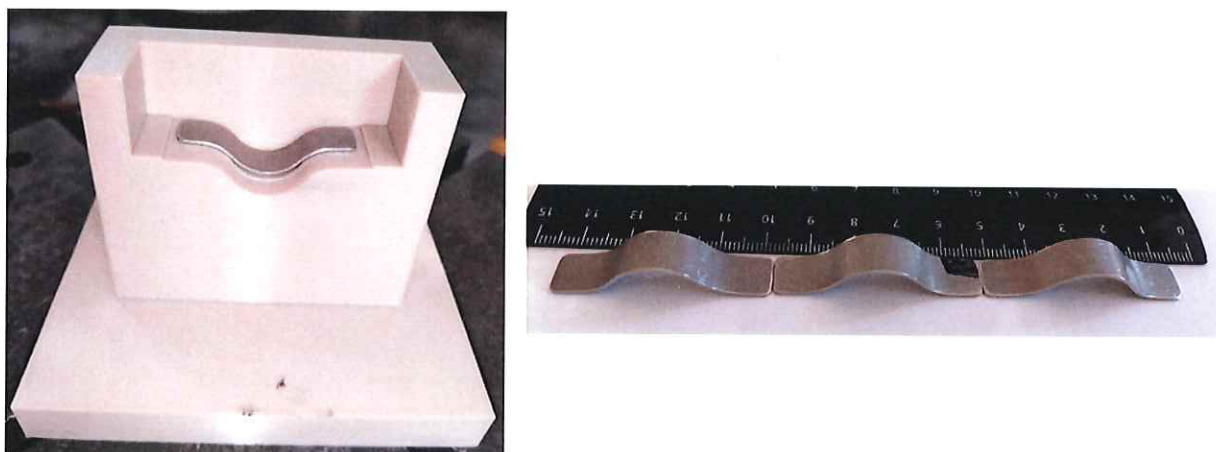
Заготовки после штамповки на гидравлическом прессе
